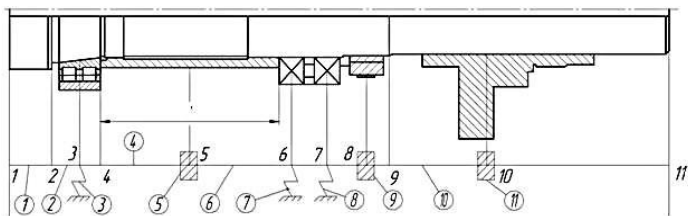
Расчетная схема шпиндельного узла консольного фрезерного станка
